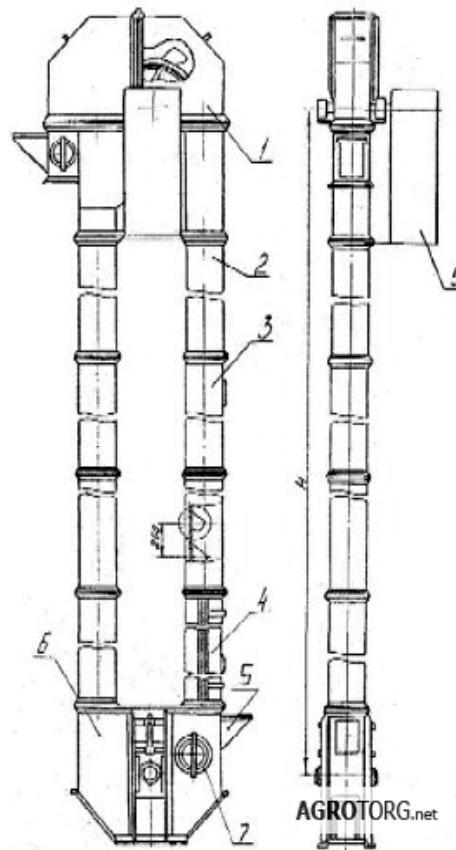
Загальний вигляд норії стрічкової ковшового, де 1 – головка; 2 – секція труби гладка; 3 – секція труби оглядова;
